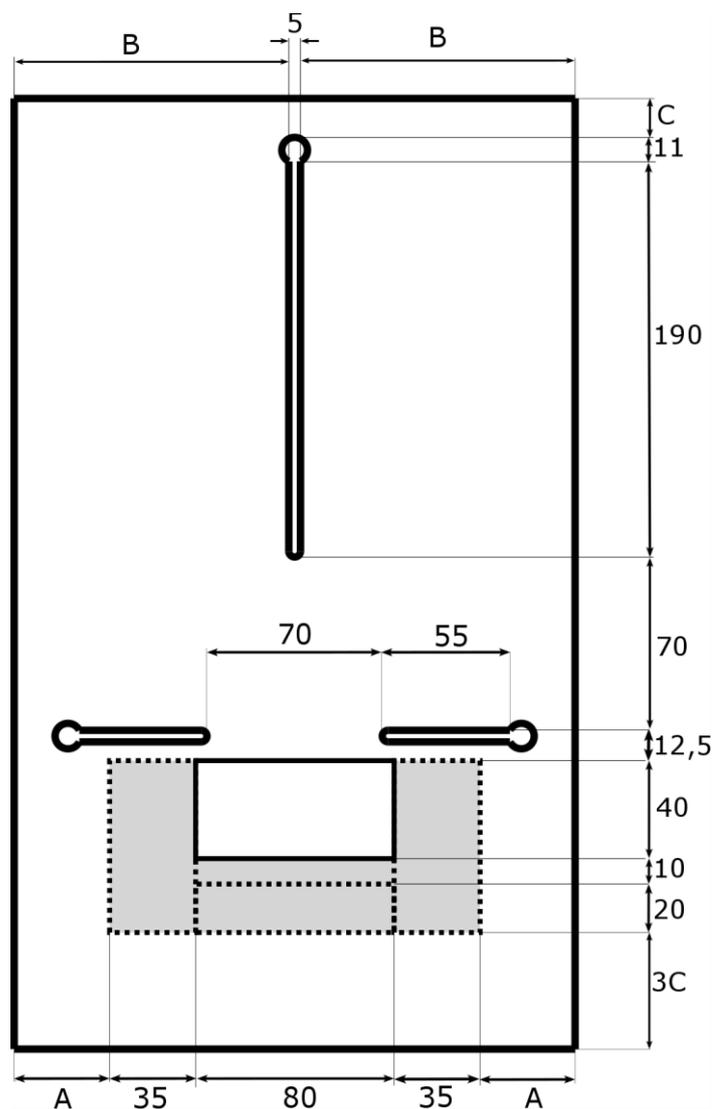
Placa de montagem. A sombreado e tracejado assinalam-se as regiões destacáveis (a quebrar no processo de instalação, se necessário). Dimensões em mm. Os valores de A e C devem garantir que a placa de montagem está ajustada às dimensões interiores da caixa.
